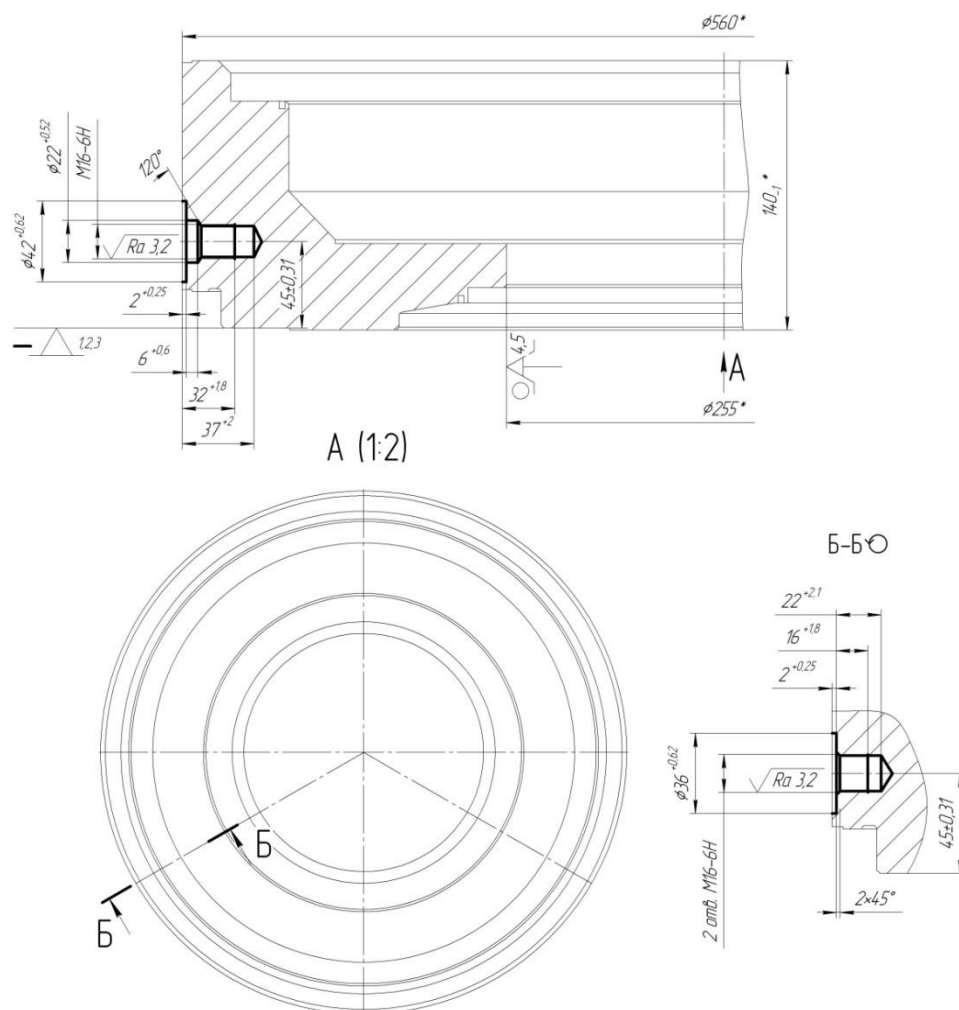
Схема базування заготовки на комплексній з ЧПК операції
